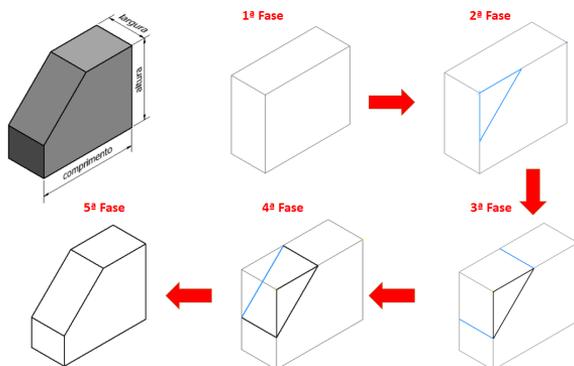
| Fases para construção de uma perspectiva: prisma com rasgo
